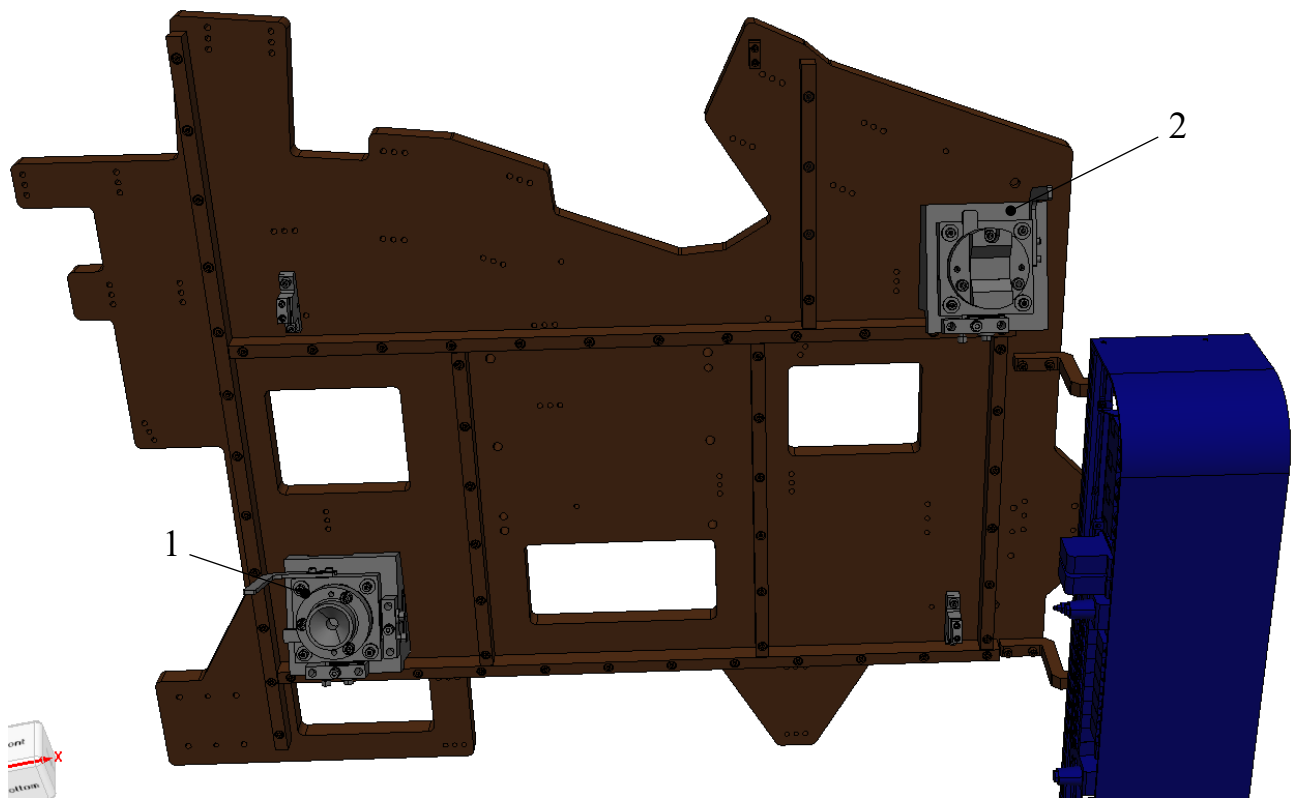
Столешница позиционирующей станции для точечной контактной сварки
